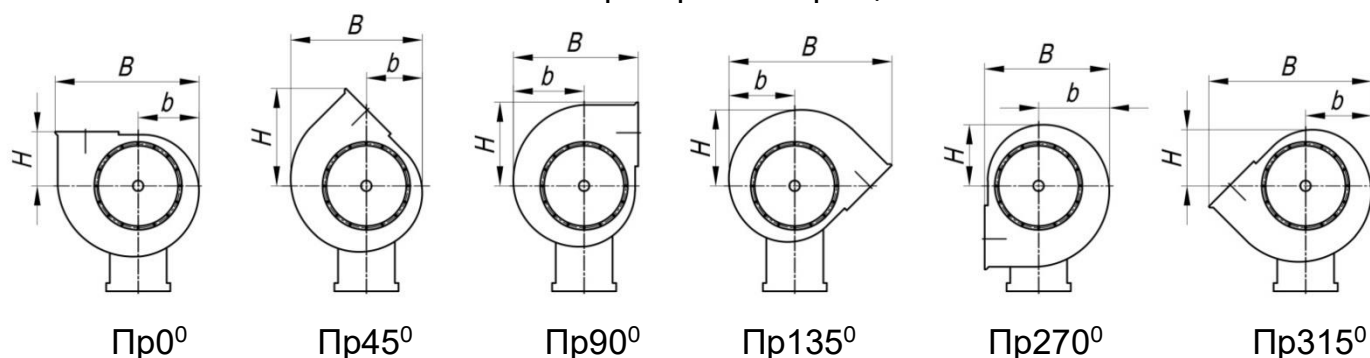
Габаритные и присоединительные размеры ВЦ 4-75 исп-5.
